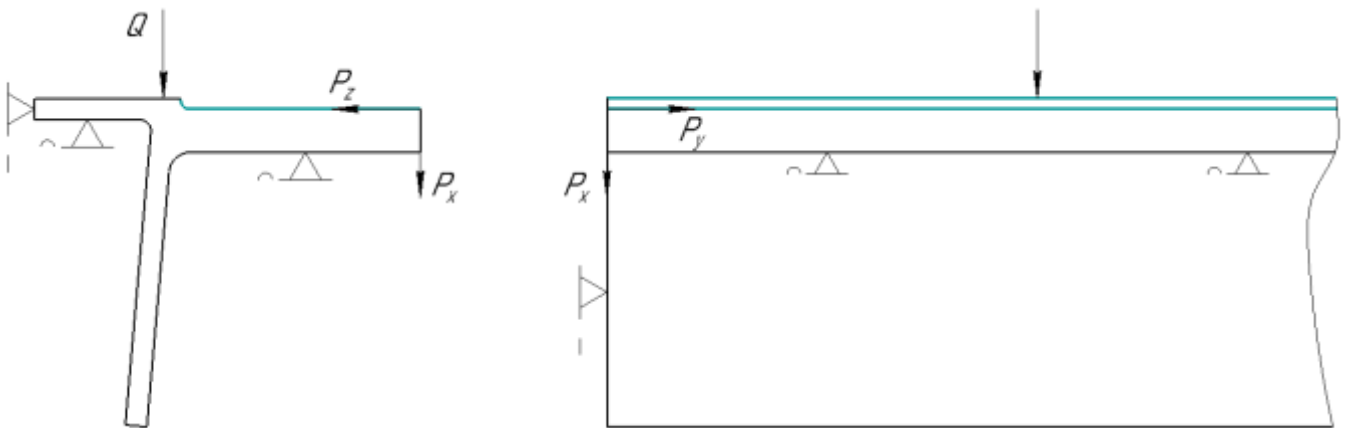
Схема діючих на заготовку сил при обробці
